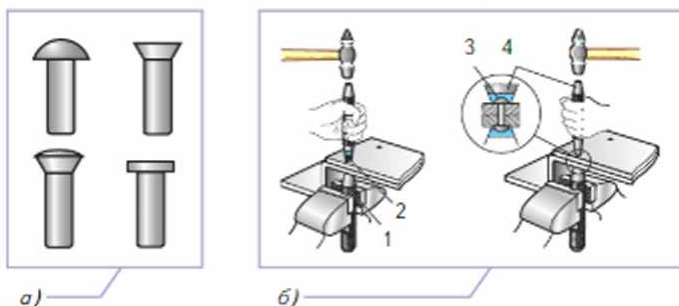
Клёпка деталей из металлов и пластмасс: а — виды заклёпок; б — технология клёпки: 1 — натяжка; 2 — поддержка; 3 — замыкающая головка заклёпки; 4 — обжимка
